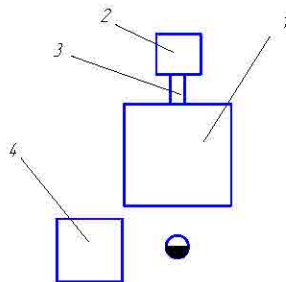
Організація робочого місця штампувальника для холодної правки: 1- гвинтовий прес; 2-тара для поковок; 3-склиз; 4-тара для заготовок.
